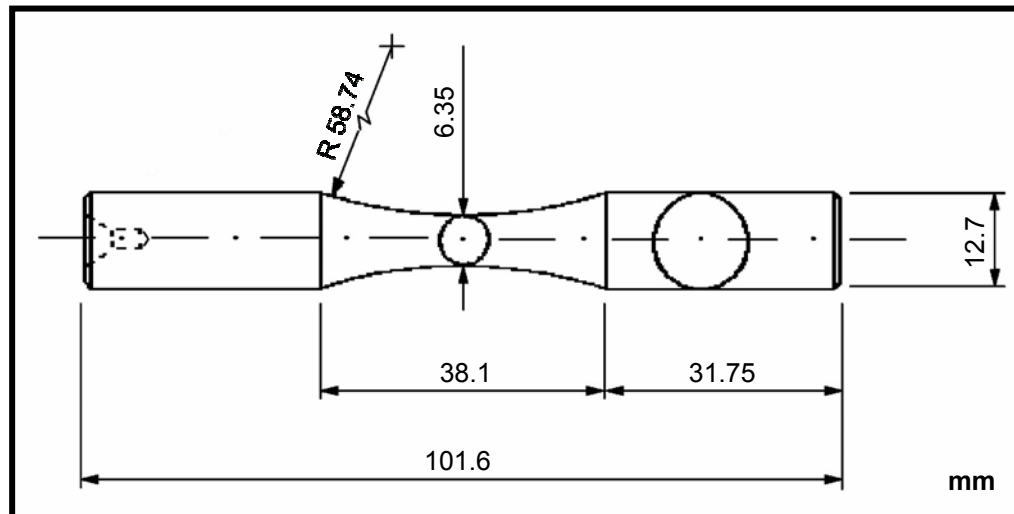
Probeta cilíndrica para ensayos de fatiga y corrosión-fatiga.
